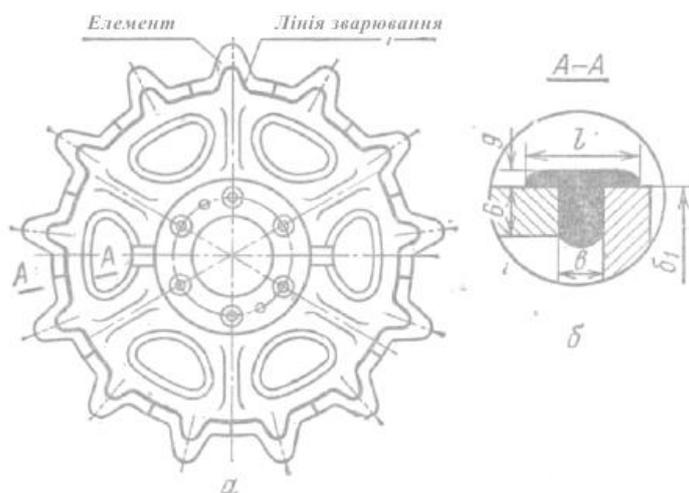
Схема зварювання вінця ведучих коліс: а – конфігурація зварювання; б – поперечний переріз зварного шва.
